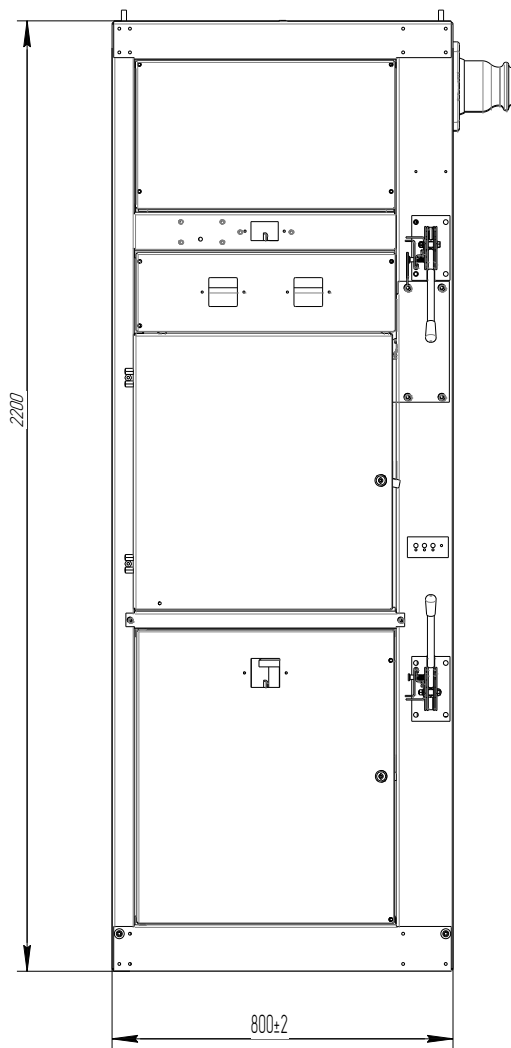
Габаритные размеры камеры КСО - 203 - 05
